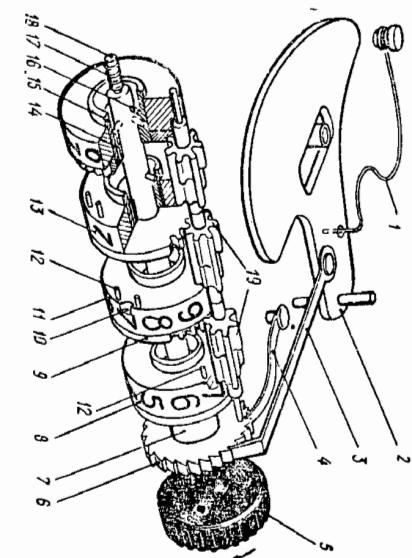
Кинематическая схема шагомера «Заря» ШМ-6:
